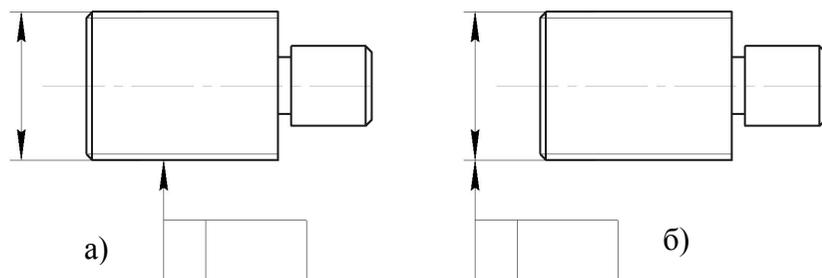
Обозначение допуска на резьбовых поверхностях
